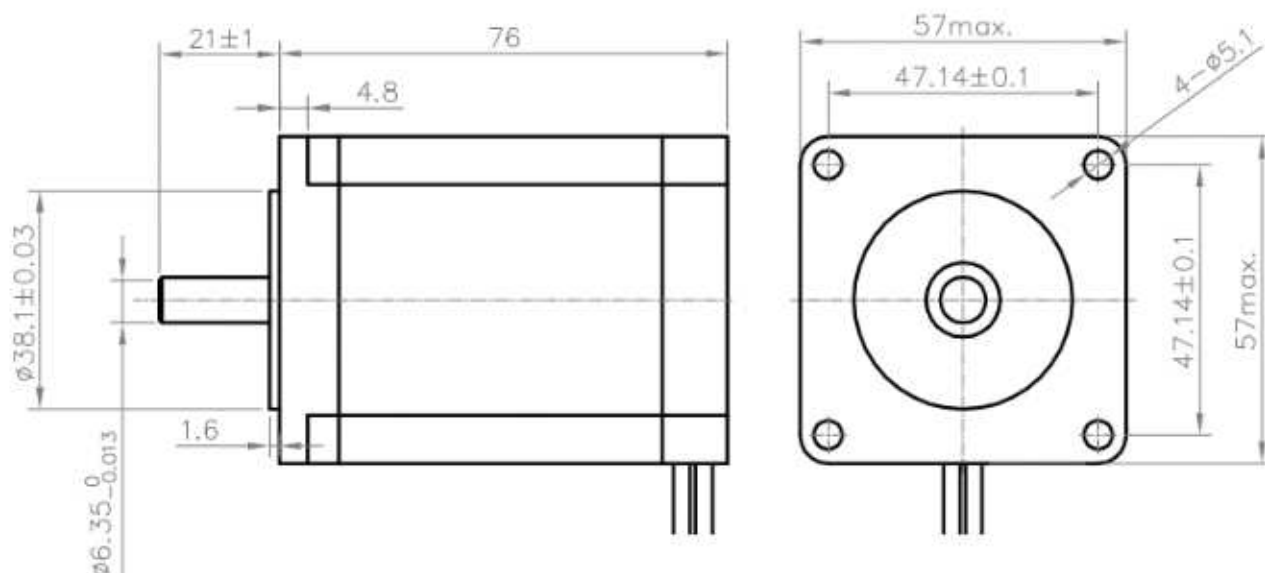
Габаритные размеры GD57STH76-2006A
